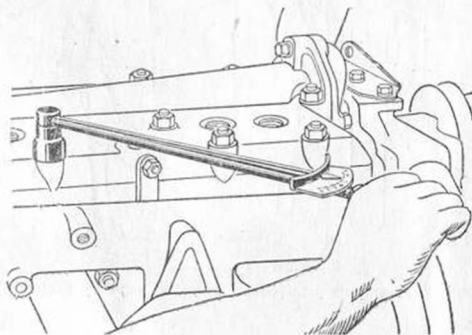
а. Подтяжка гаек крепления головки цилиндров с помощью ключа с динамометрической рукояткой.
